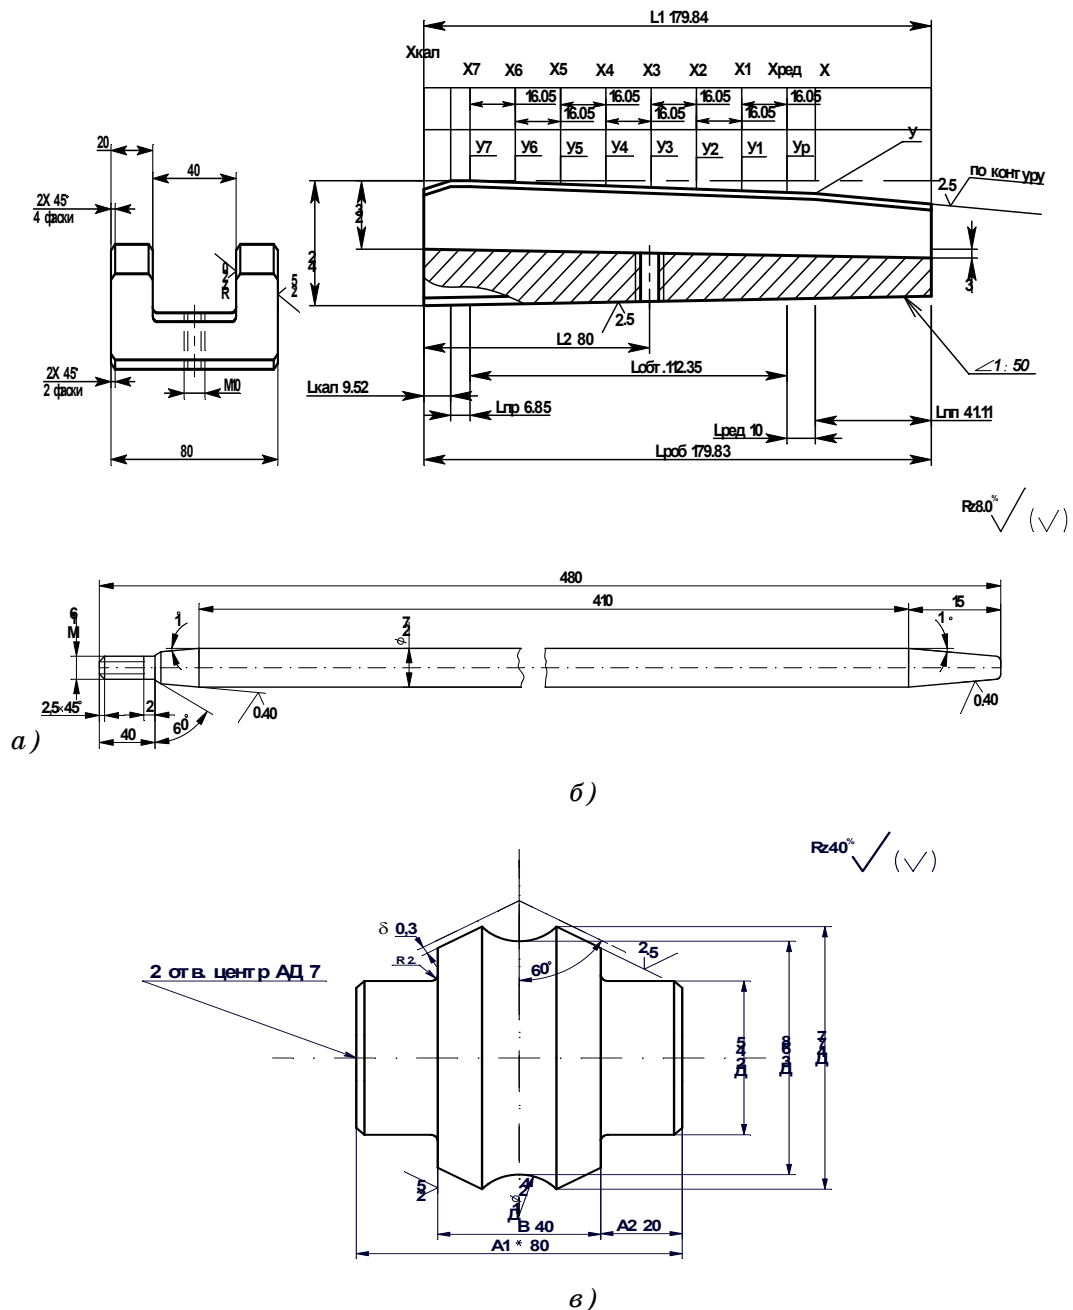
Приклад інструмент стану ХПТР розробленого за допомогою САПР ХПТР: а – планка; б – оправка; в – ролик.
